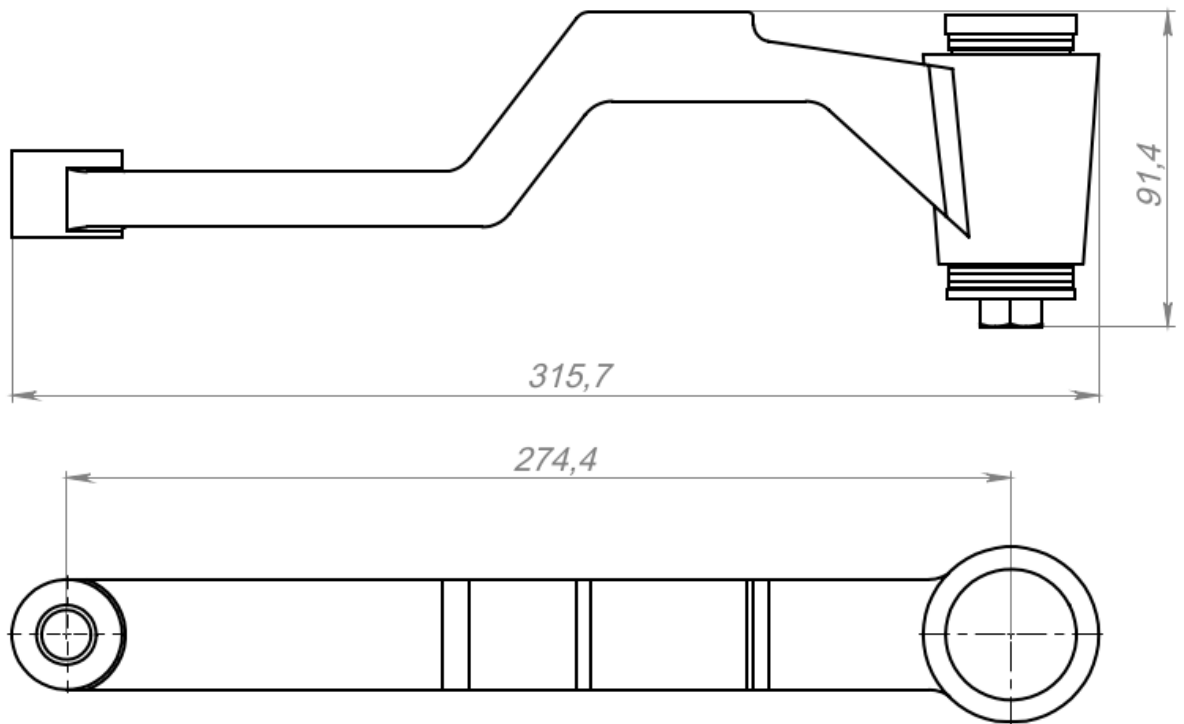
Важіль опорного колеса сошника з трибоспряженням
